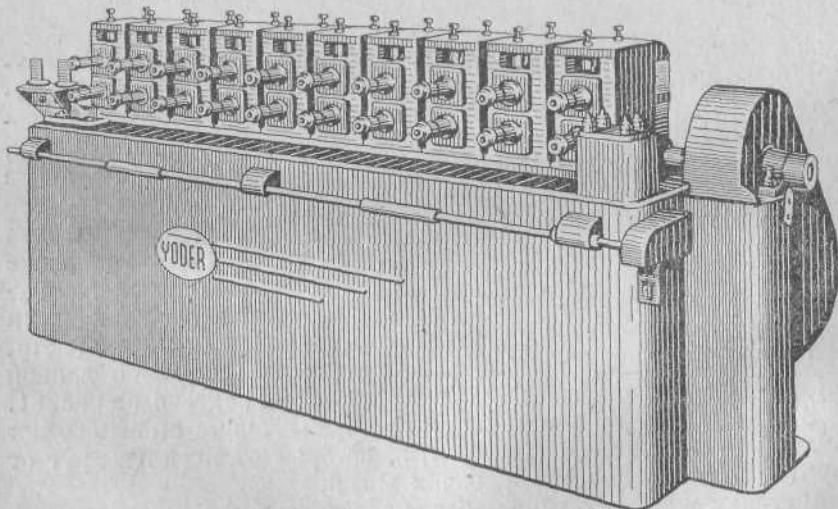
Профилегибочный стан открытой конструкции (консольный).
